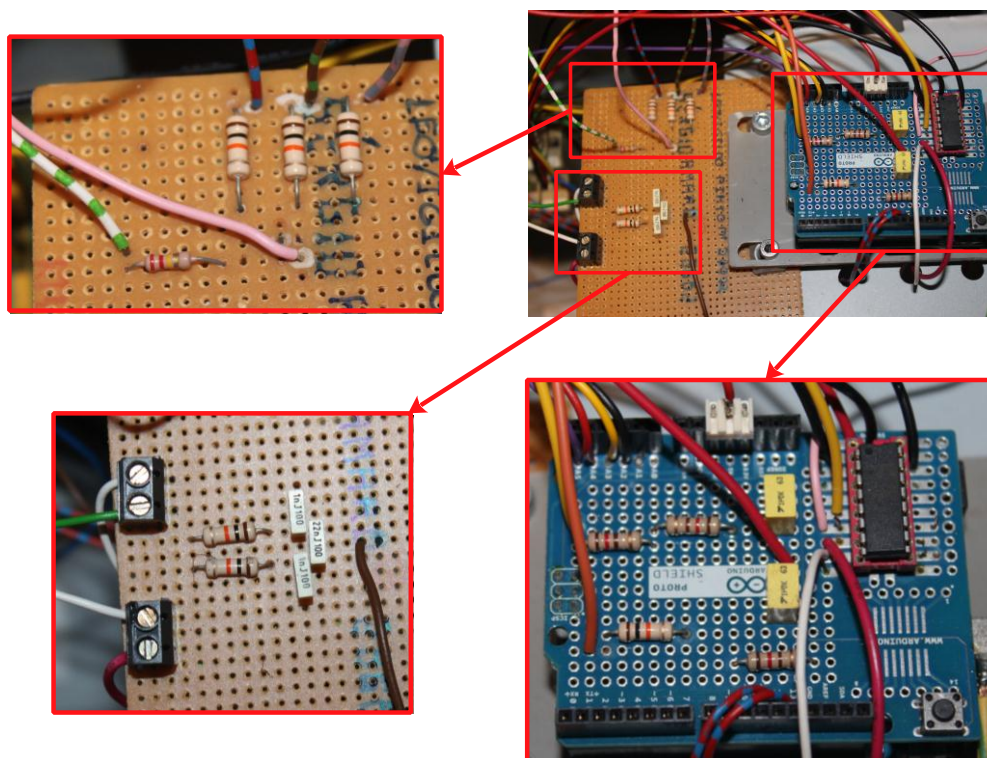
Placa Arduino *Proto Shield* com componentes elétricos soldados.
